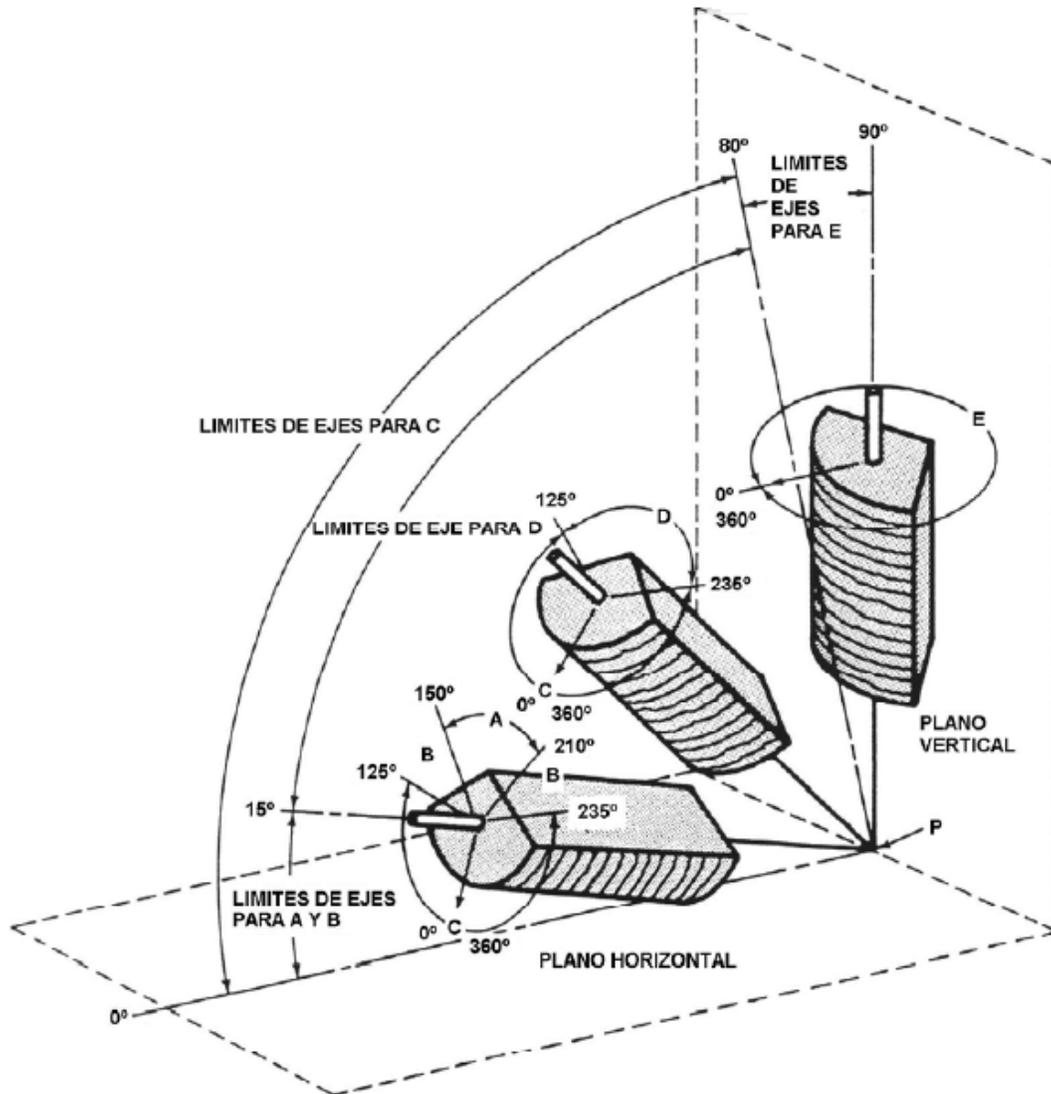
ORIENTACIÓN DE LAS SOLDADURAS EN FILETE. QW-461.2.
